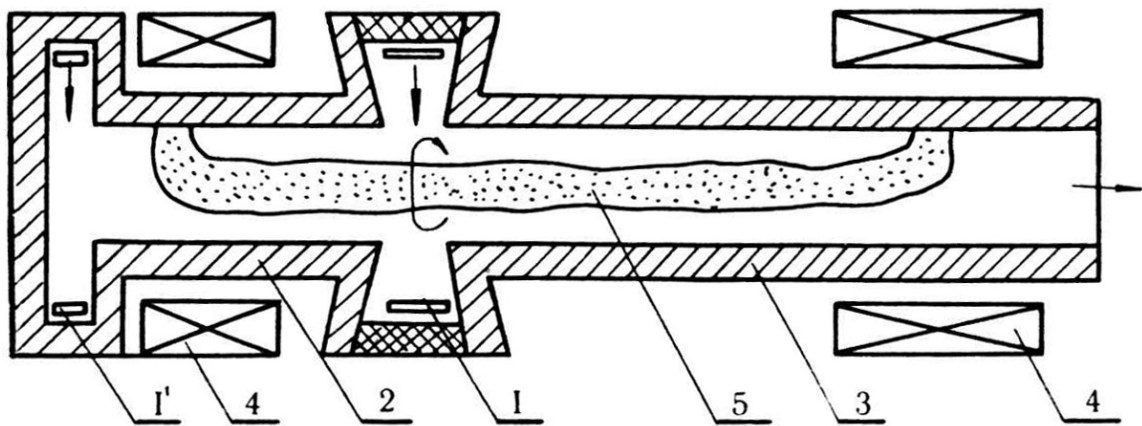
Двухкамерный плазмотрон с газовой вихревой стабилизацией дуги:
